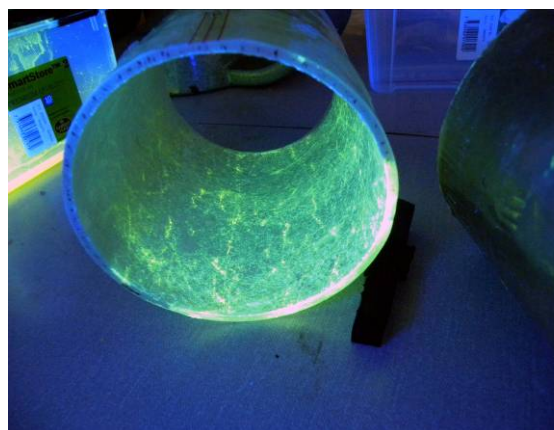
Provet efter behandling med penetrant (20 min) och torrframkallare (20 min).
